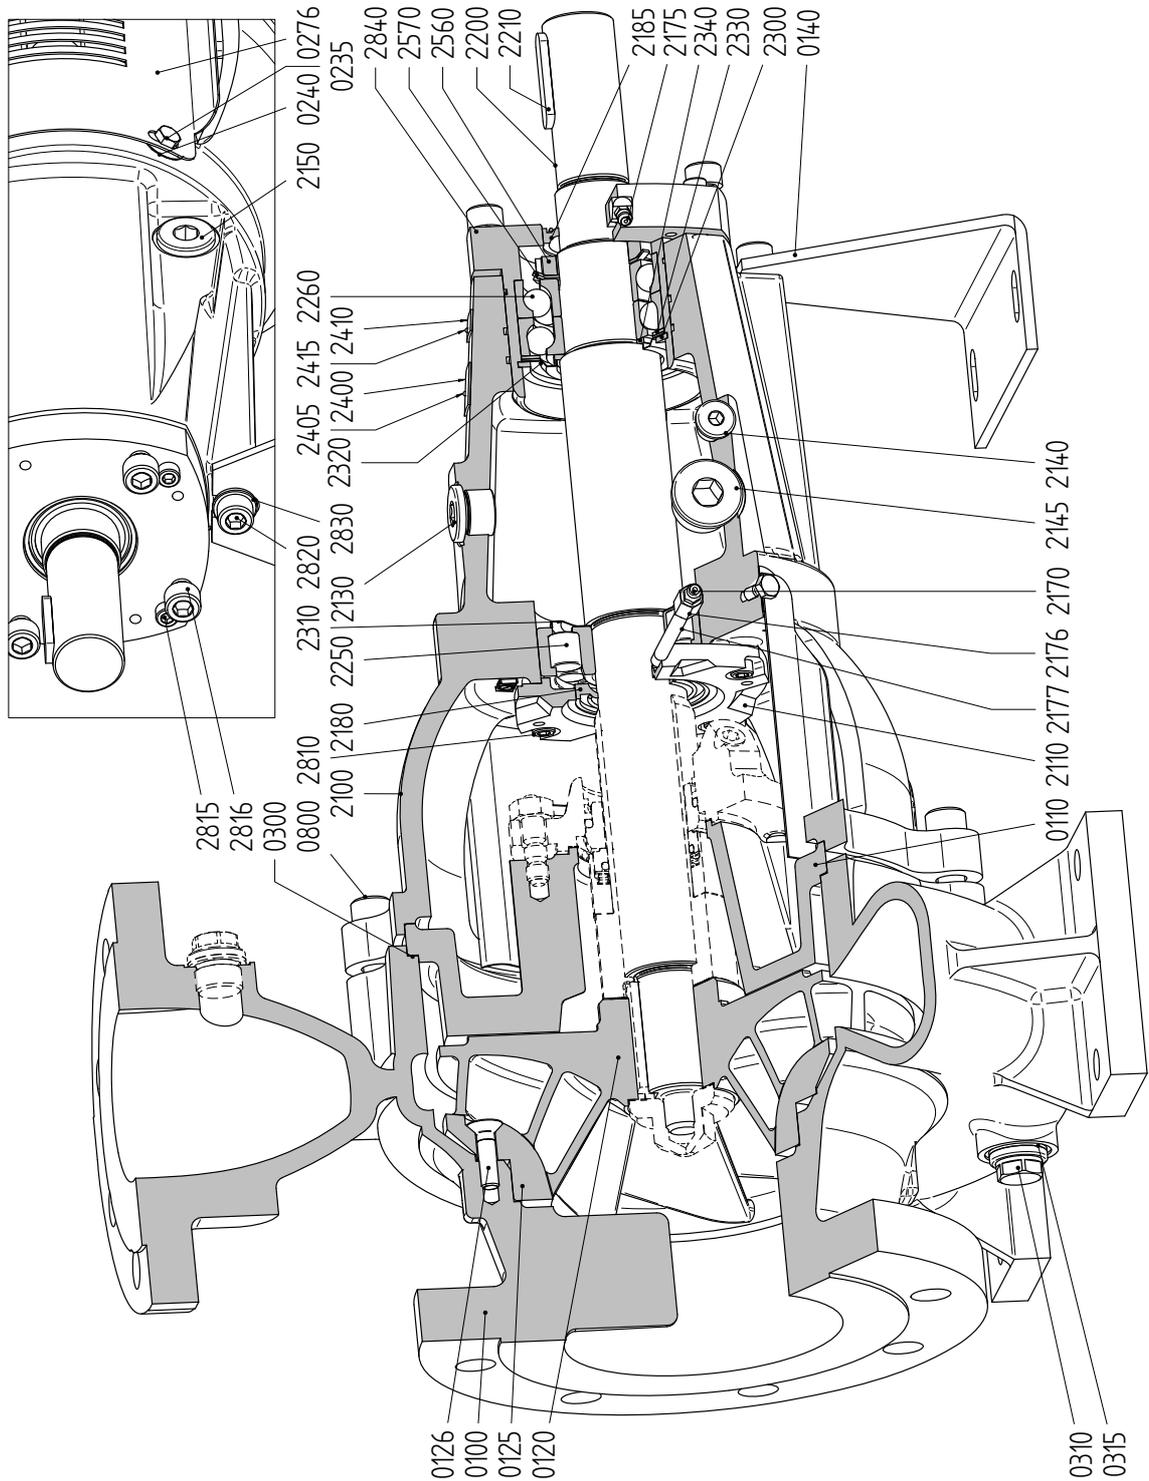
Schnittzeichnung L5 mit konischer Bohrung.
